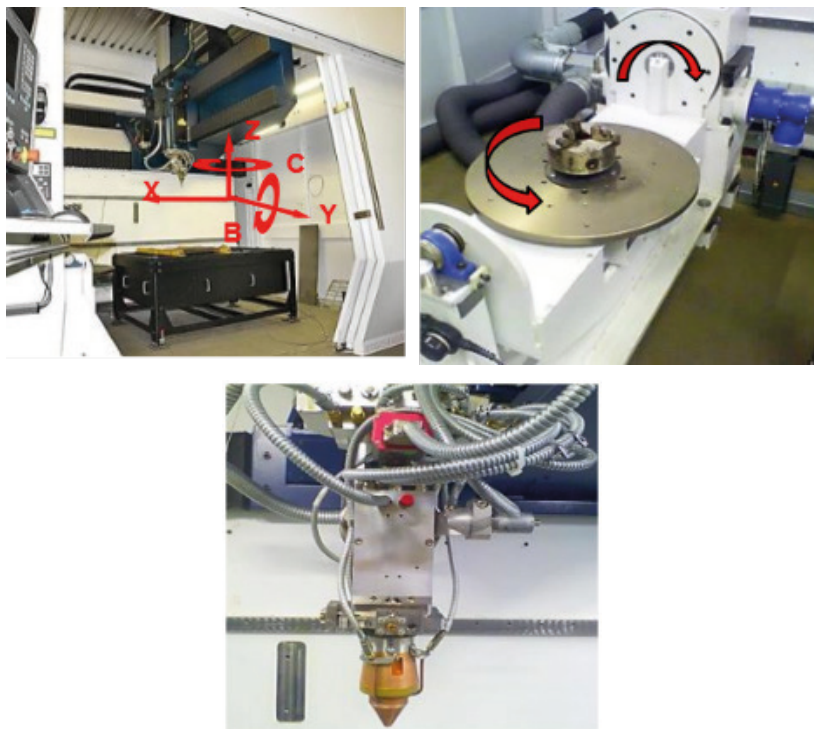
Обрабатывающий центр TruLaser Cell 7020
